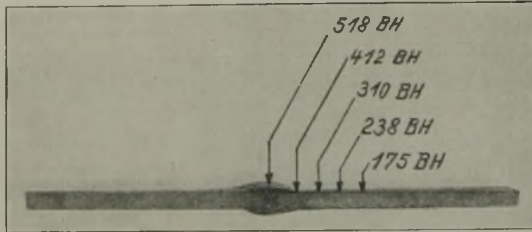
Härteverlauf einer an der Luft abgekühlten Verbindungsschweißung von rostfreien Chromstahlblechen in Brinelleinheiten.
